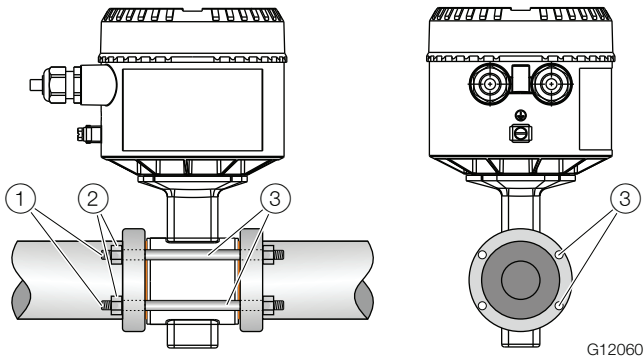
Conjunto para montagem de flange intermédio (Exemplo)
